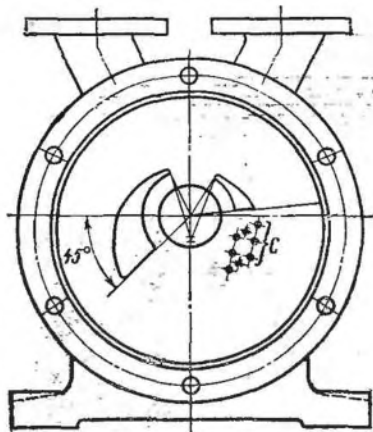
Вид на торцовую крышку со стороны рабочего колеса
